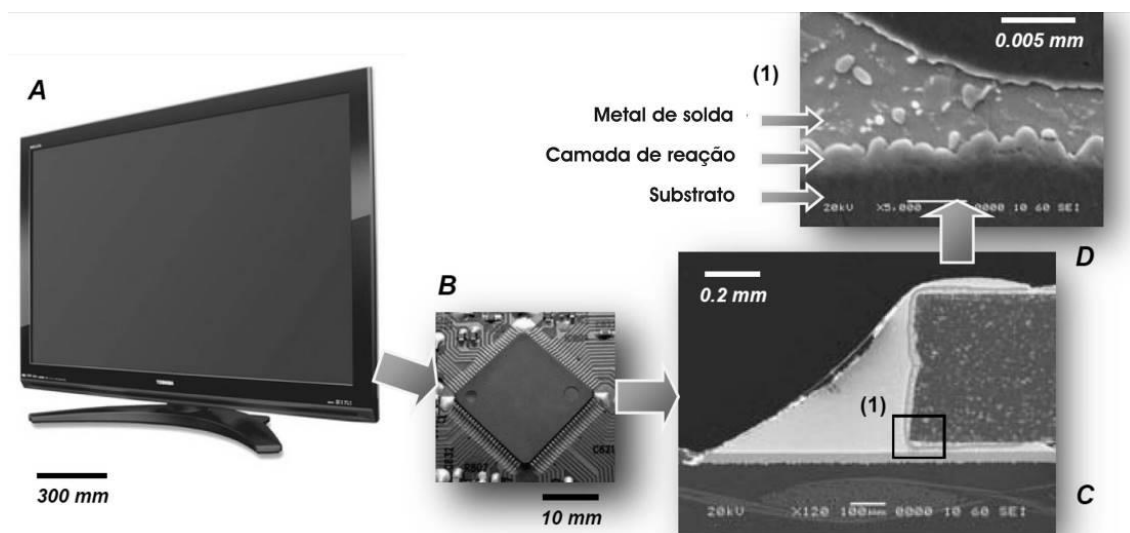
Diferentes escalas envolvidas na soldagem de microeletrônicos: (A) equipamento eletrônico (monitor), (B) processador soldado a uma placa de circuito impresso, (C) seção transversal da junta soldada, e (D) detalhe da interface entre a liga de solda e o substrato [69].
